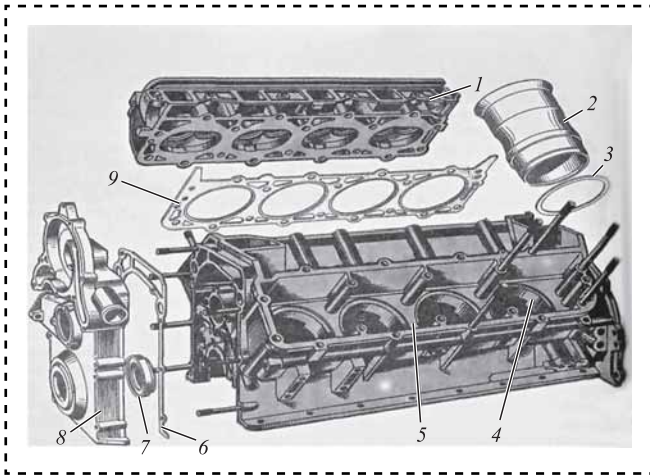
Головка и блок цилиндров V-образного восьмицилиндрового двигателя ЗМЗ-53:
